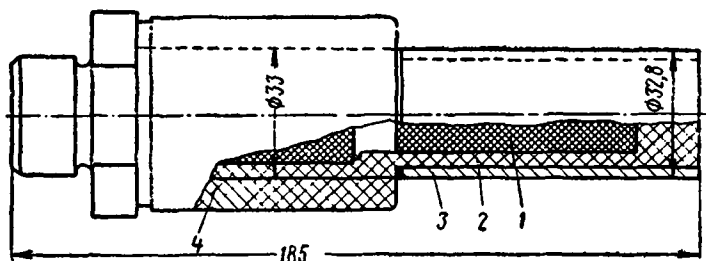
Кронштейн щеткодержателя тягового двигателя НБ-412М, изолированный пресс-массой АГ-4В:
